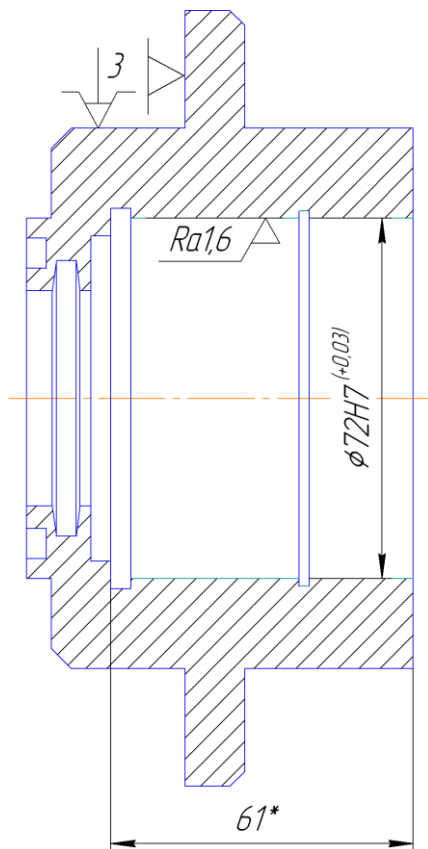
Ескіз на обробку поверхонь 11, 12  $\text{Ø72H7}^{(+0,03)}$  фланця 943.73.1133.02.00.017
